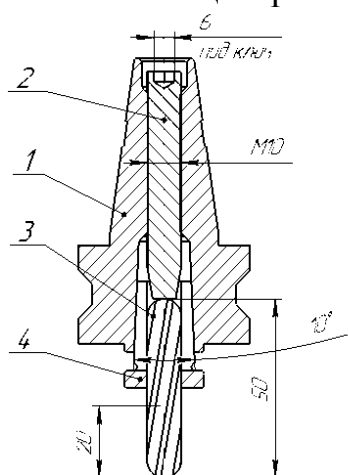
Фреза для станка с ЧПУ: 1 – корпус, 2 – винтовой упор, 3 – твердосплавная вставка, 4 – разрезная втулка
